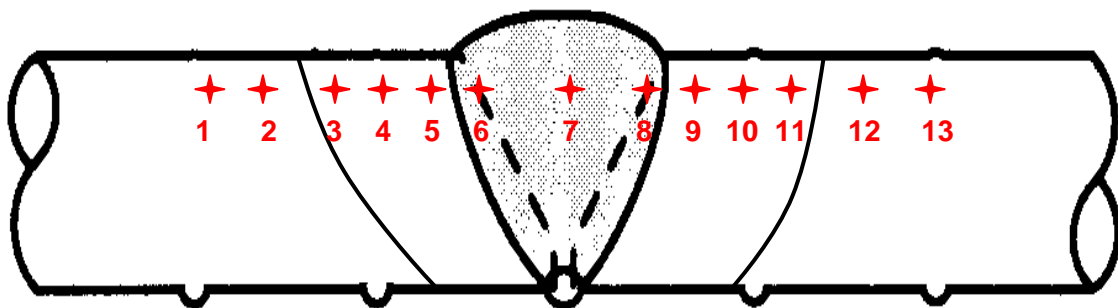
Esquema de Barrido de Durezas en Barra Soldada.
